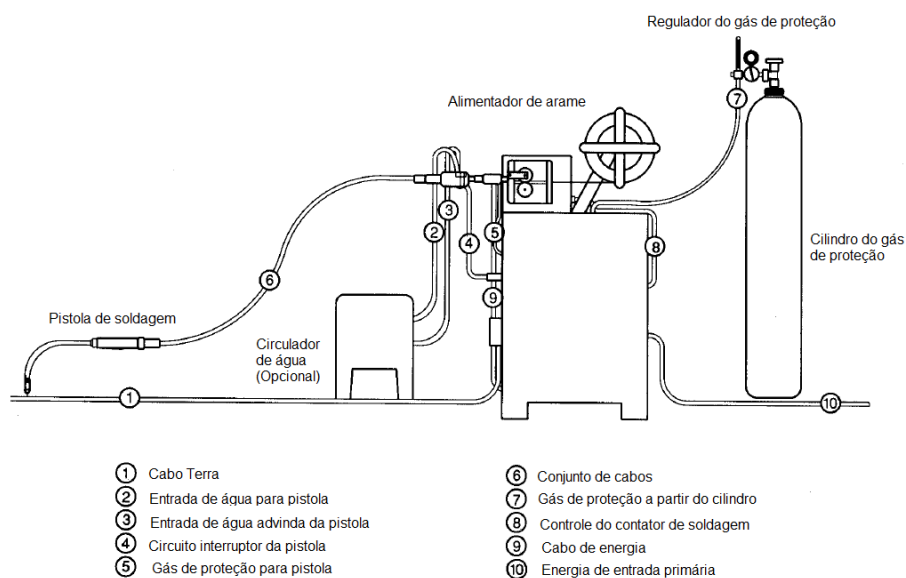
Esquema do equipamento de soldagem MIG/MAG [16].
